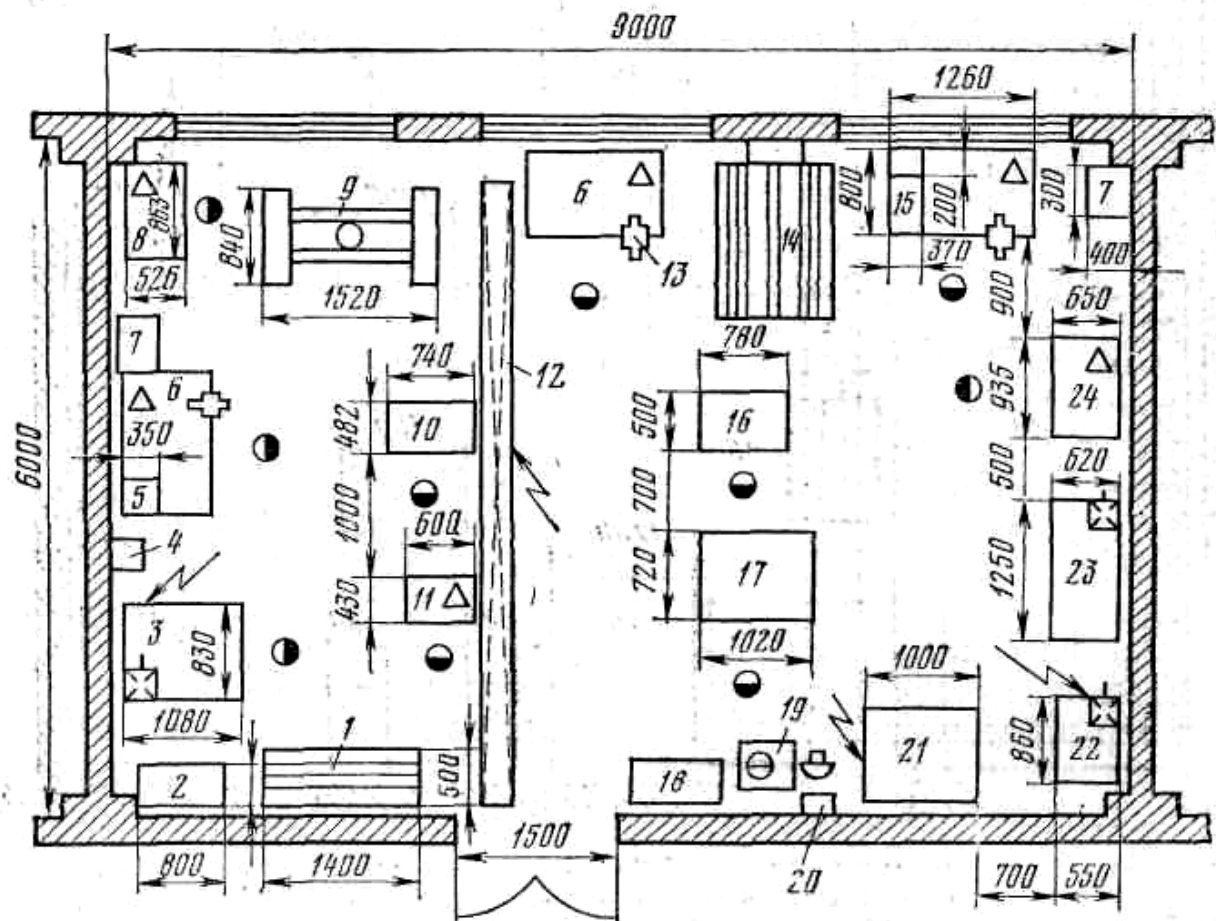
Планировка отделения и рабочих мест слесарей по ремонту агрегатов: 1 — стеллаж для деталей; 2 — ларь для обтирочных материалов; 3 — станок для расточки тормозных барабанов; 4 — телефон и радио; 5 — радиально-сверлильный настольный станок; 6 — слесарный верстак; 7 — настенный шкаф для приборов и инструментов; 8 — стенд для разборки и регулировки сцеплений; 9 — гидравлический пресс 40 т; 10 — стенд для ремонта редукторов задних мостов; 11 — стенд для клепки тормозных накладок; 12 — подвесная край-балка; 13 — тиски; 14 — стеллаж для инструментов; 15 — настольно-верстачный пресс, 3 т; 16 — стенд для ремонта коробок передач; 17 — стенд для ремонта передних и задних мостов; 18 — ларь для отходов; 19 — раковина для мытья рук; 20 — электрический рукосушитель; 21 — вертикально-сверлильный станок; 22 — заточный станок; 23 — передвижная моечная ванна; 24 — стенд для ремонта карданных валов и рулевых механизмов
